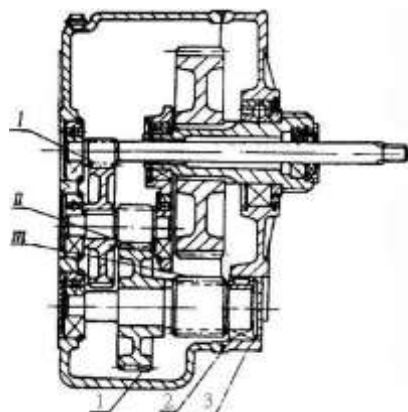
Редуктор подъема, Крышка коробки, Овальная маслoneпроницаемая прокладка по контуру, Корпус коробки
